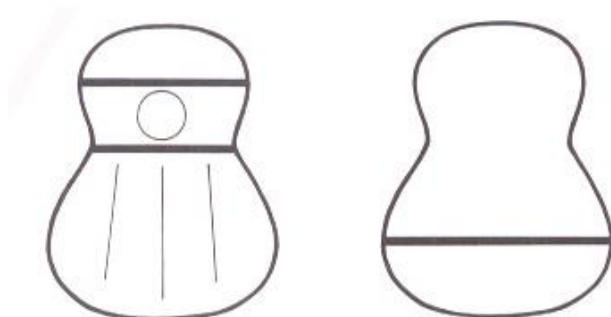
Esquema de refuerzos en tapa y fondo²⁰⁰
